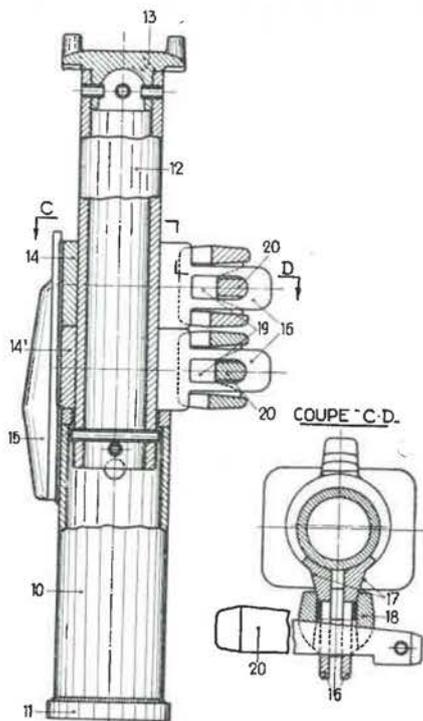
Coupe montrant le détail de la serrure et de l'étau Schwarz.
